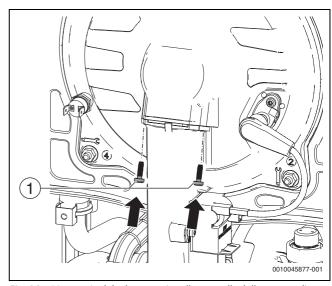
Montaggio del tubo gas-aria sullo sportello della camera di combustione
